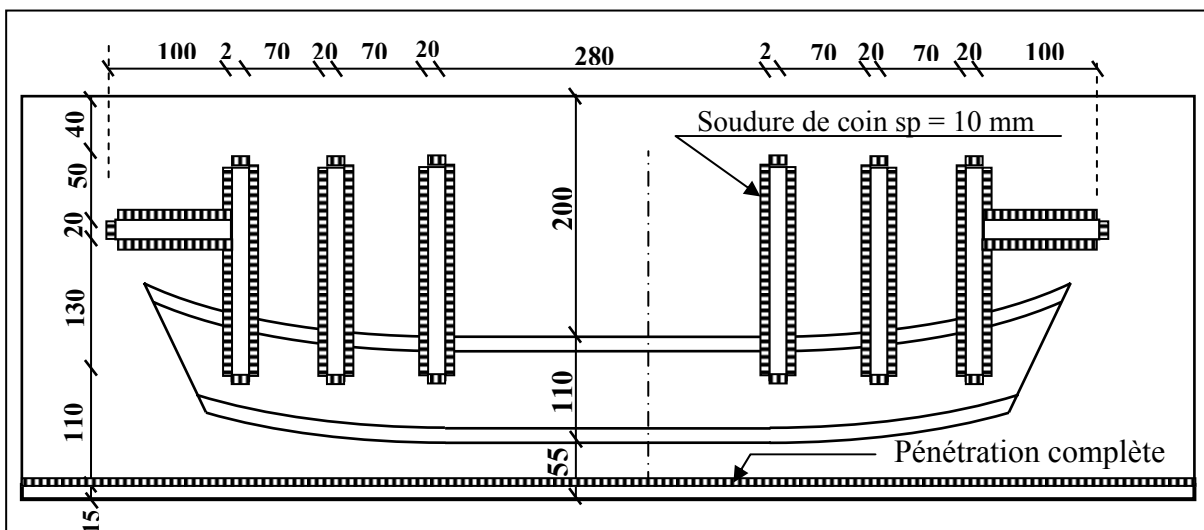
Assemblage des différents éléments par soudure
